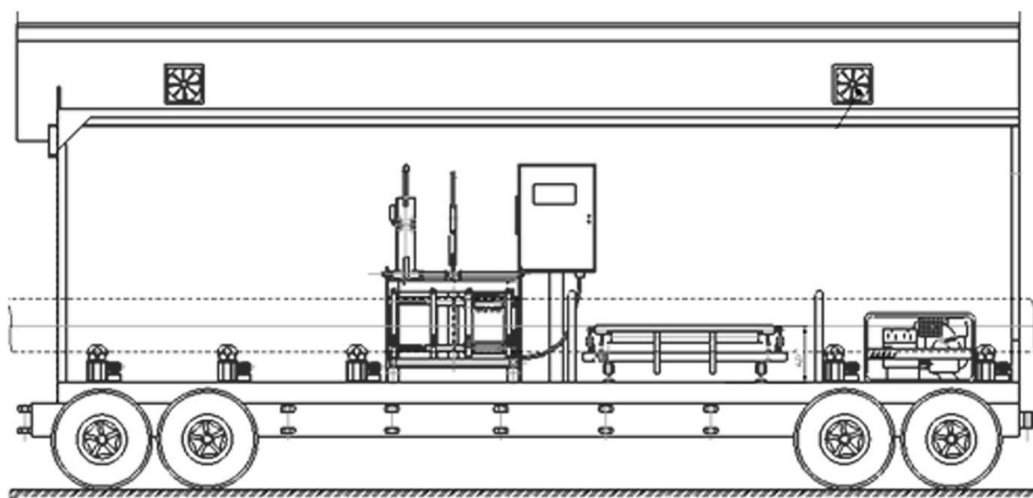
Платформа комплекса со сварочной установкой
